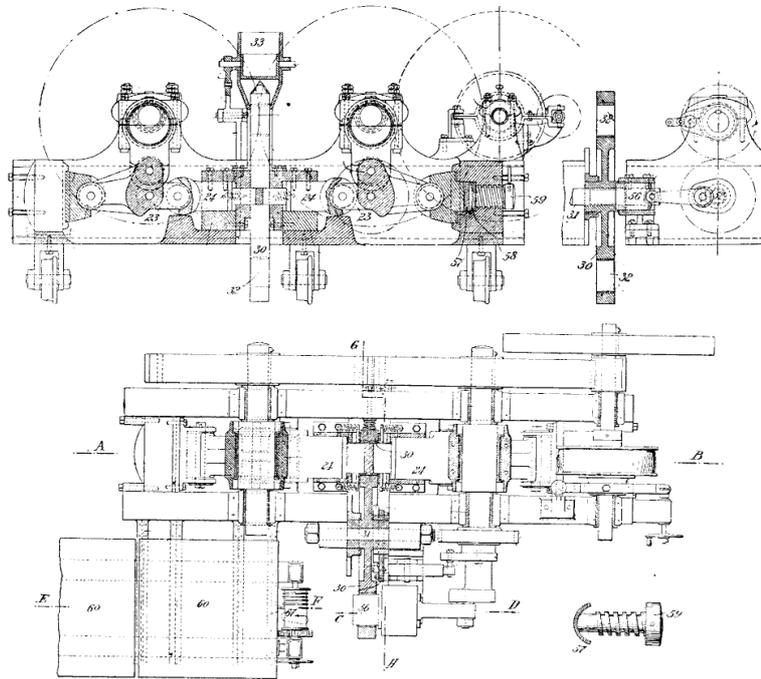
à 4. — Presse Wyssling. Coupes A B et G H. Plan et détail.
